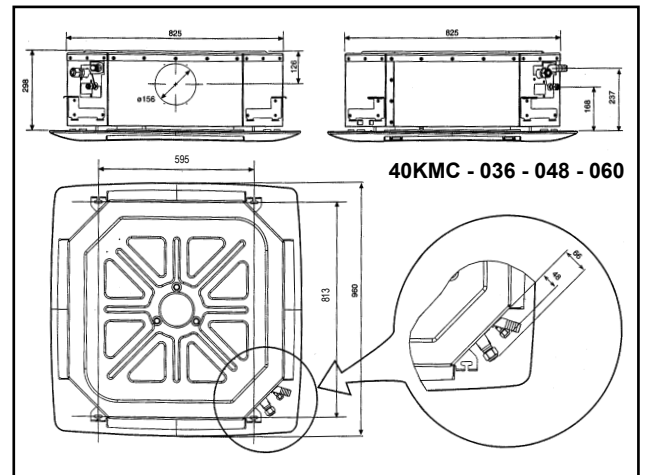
DIMENSIONAL 40KMC - 036-048-060
